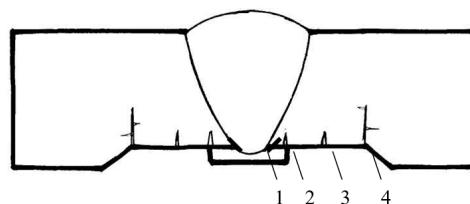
Усталостные трещины, образующиеся в сварных соединениях паропроводов: 1 – на участке сплавления; 2 – на участке перегрева; 3 – на участке перекристаллизации; 4 – на сопряжении разнотолщинных элементов
